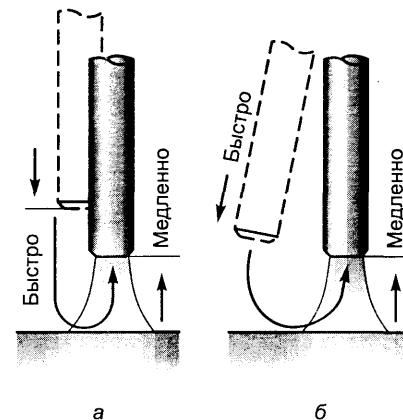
Способы зажигания сварочной дуги
